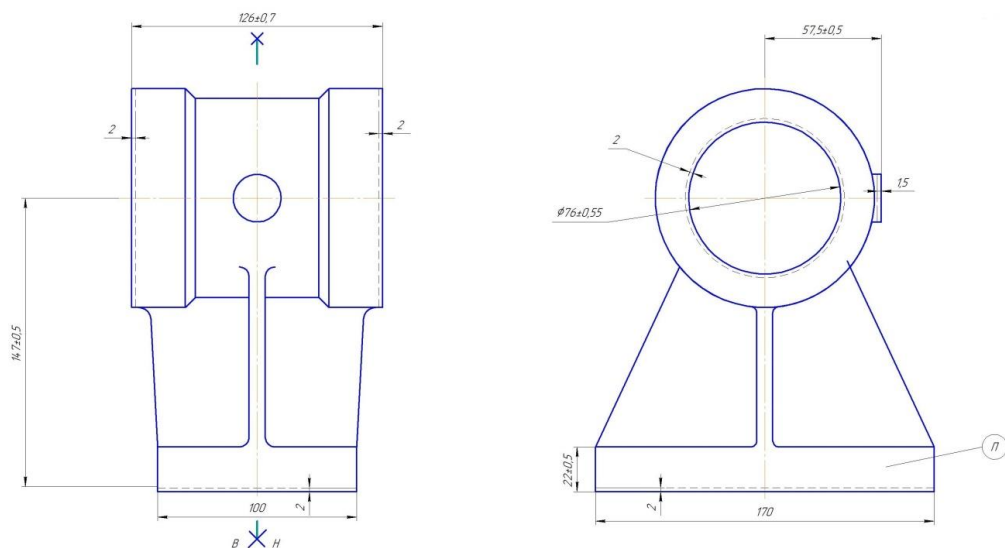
Ескіз заготовки для деталі «Корпус»
